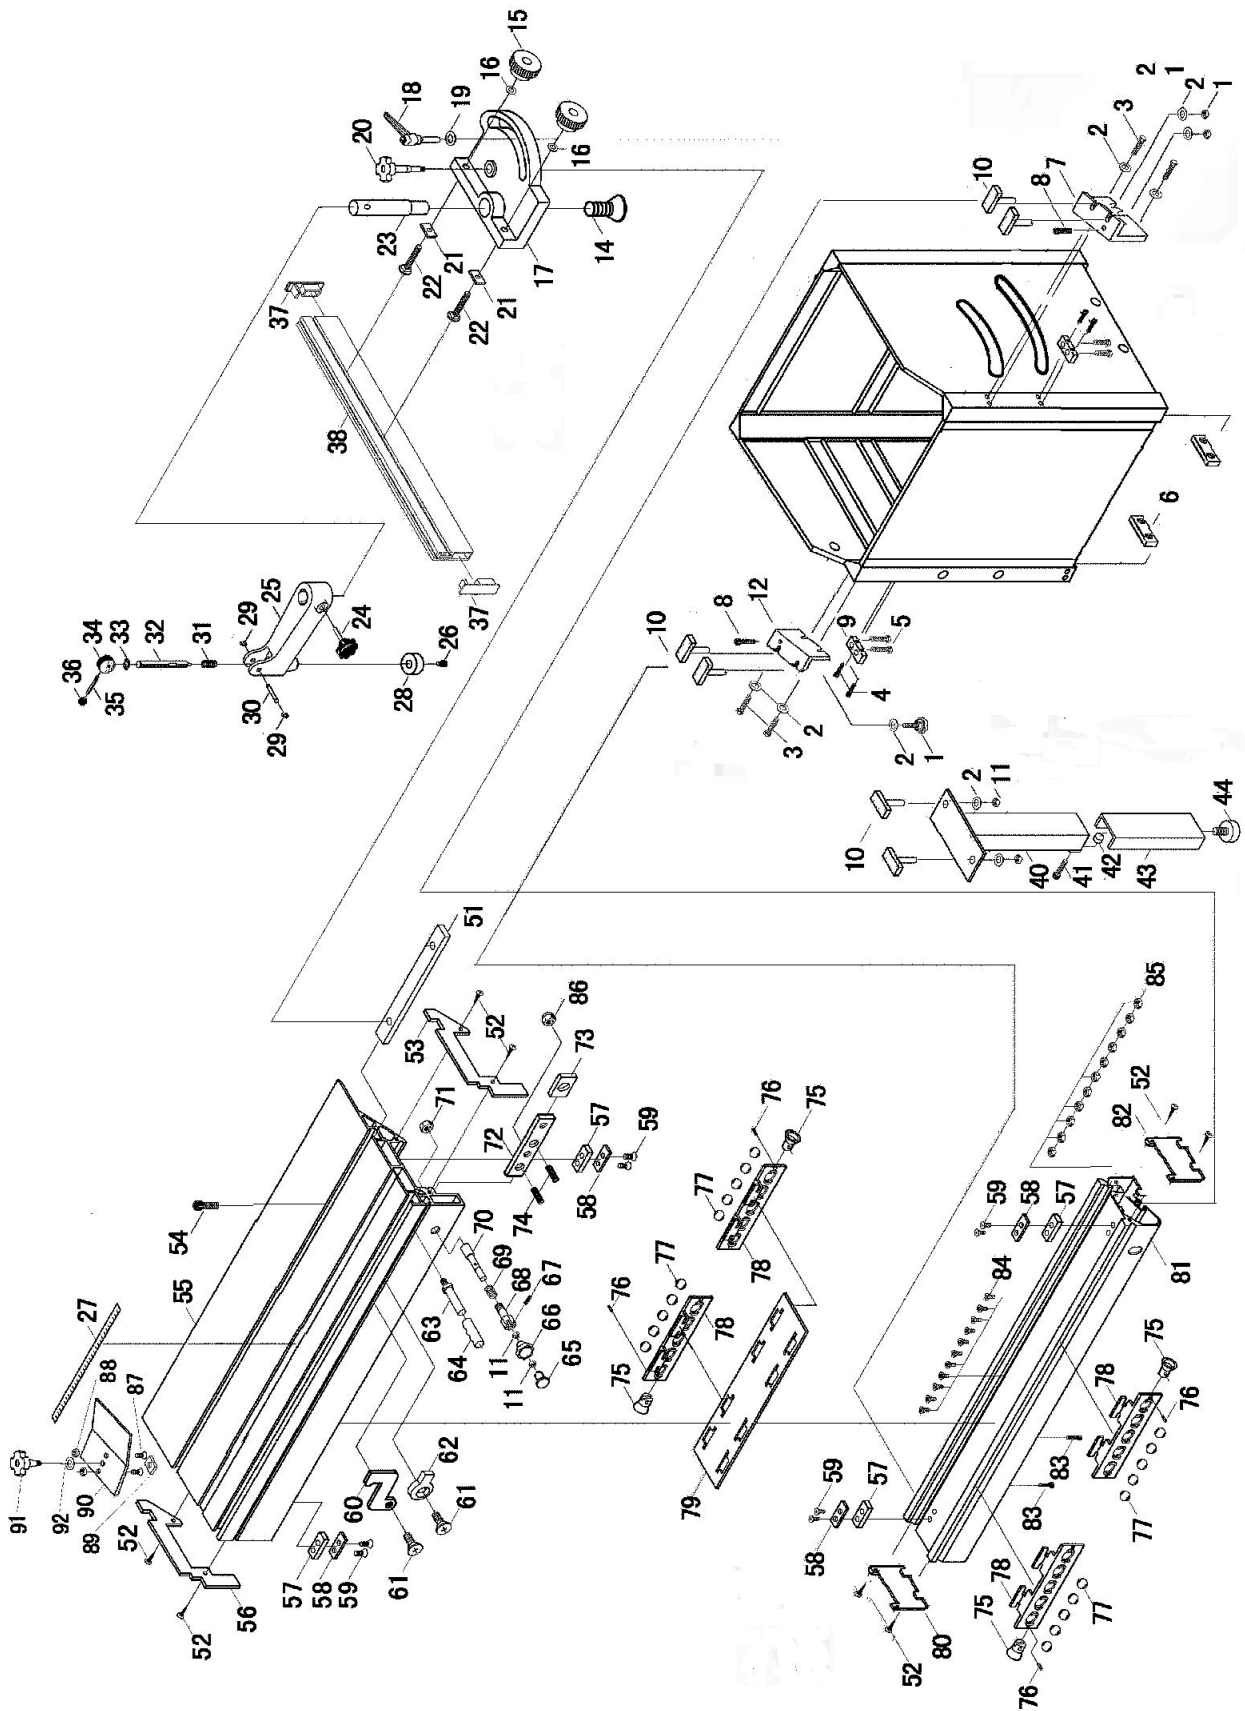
Dessin des pièces détachées 2 - Scie à format FKS 315-2000 E
